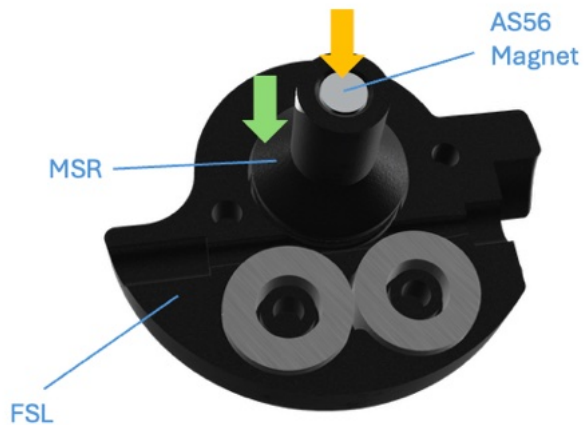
Rewinder-Chassis Montageschritt 15.
